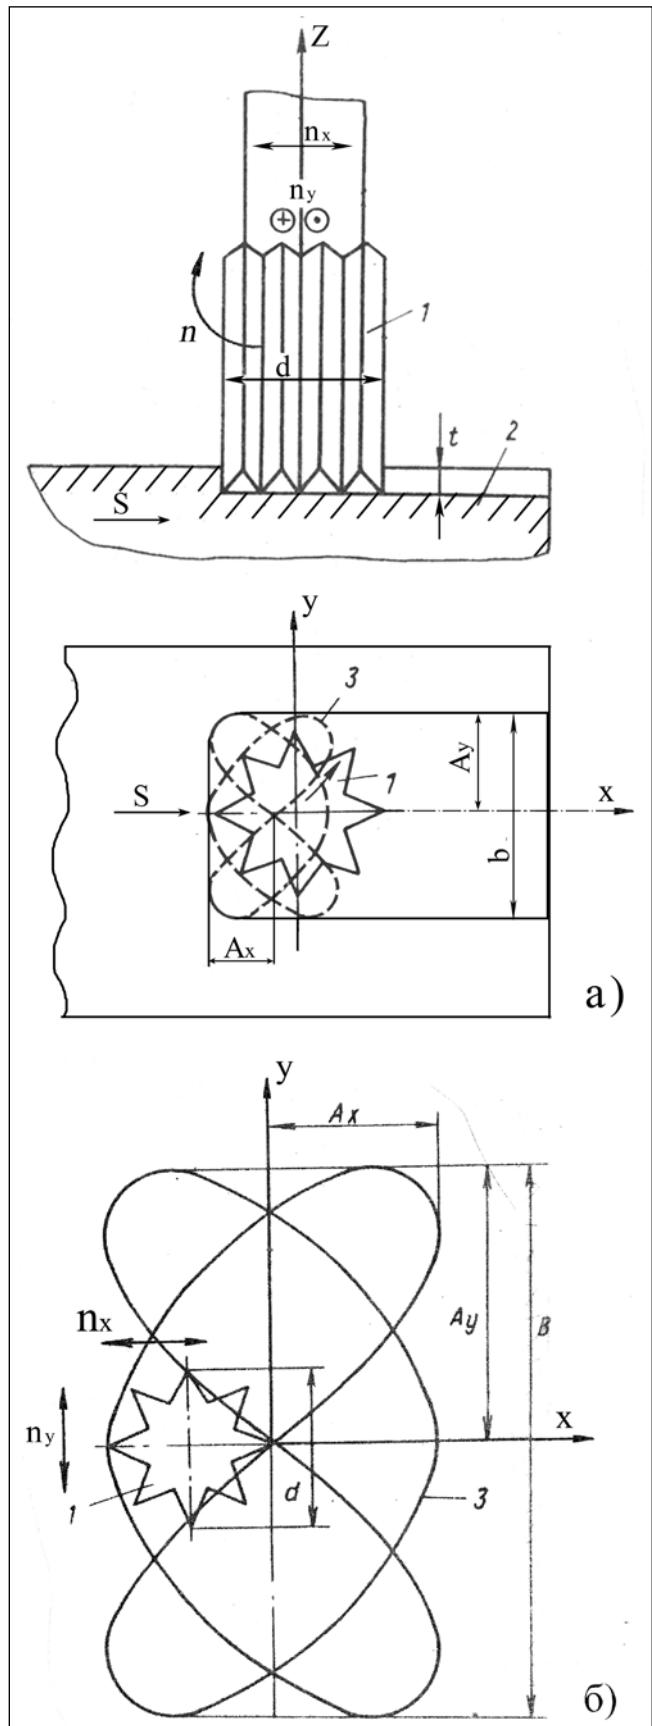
Фрезерование концевой фрезой: а) схема, б) траектория движения
